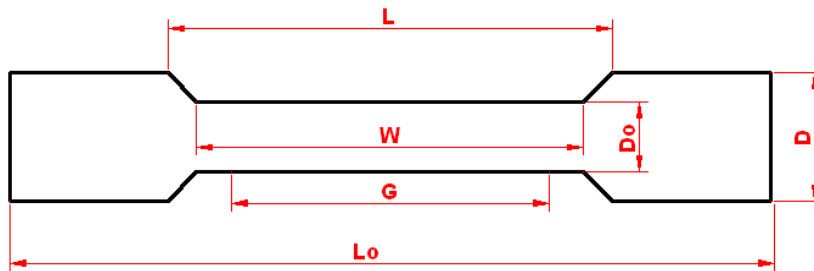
Probeta normalizada para un ensayo de tracción. (Fuente Piñeiro, 2009)
